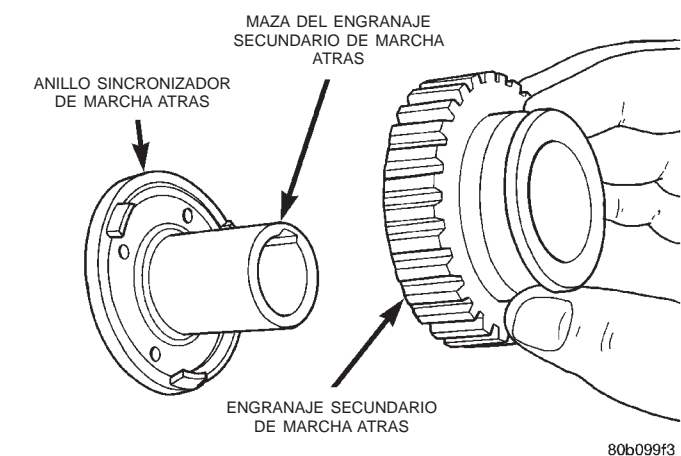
Desmontaje del engranaje secundario de marcha atrás
